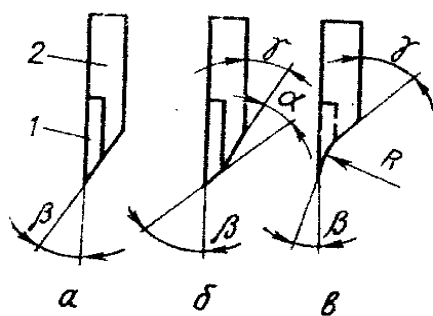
Конструкции режущего ножа и способы его заточки:
